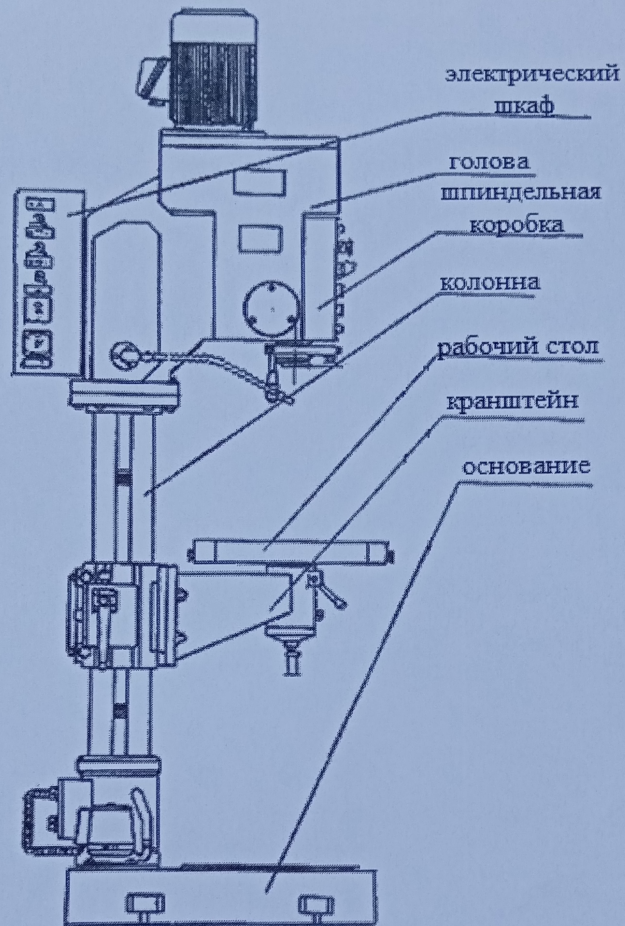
Общий вид станка Z5040B с обозначением составных частей станка и органов управления.
